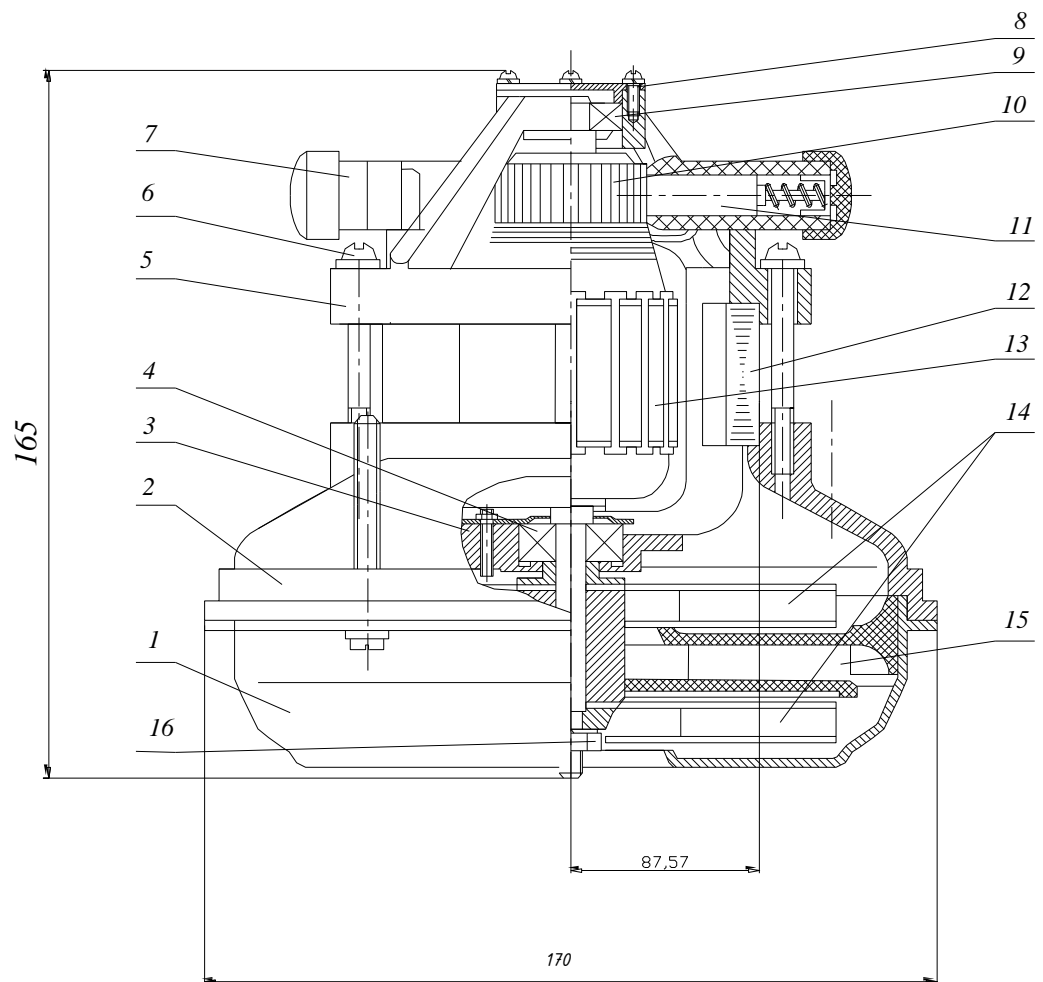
Загальний вигляд всмоктувального агрегату ВВА-600
